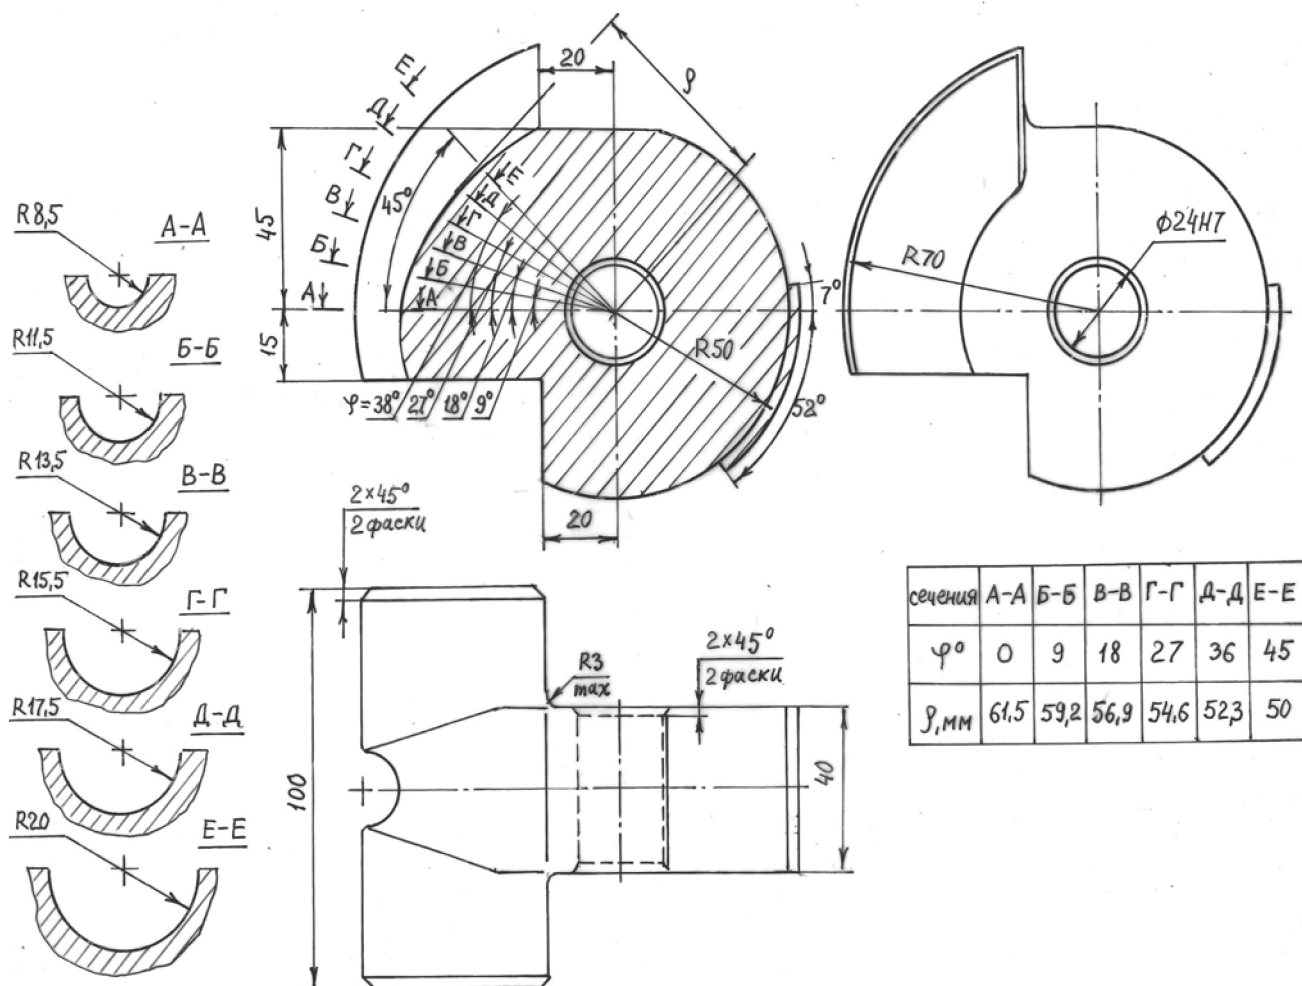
Чертеж вальца, образующего половину полости матрицы штампа
